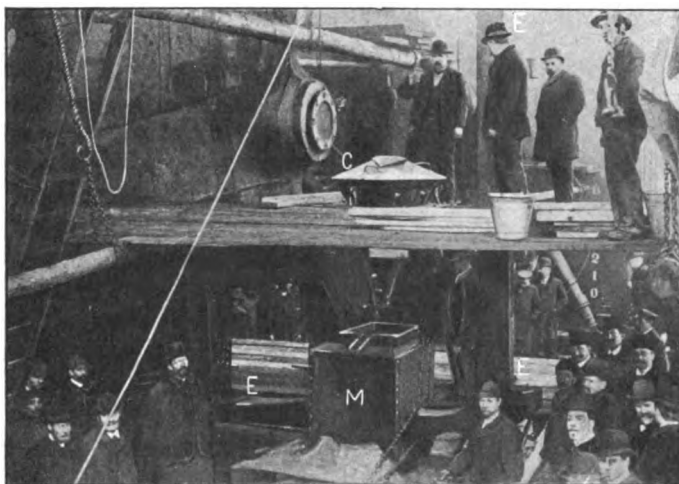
Réparation de l'étambot du Sevilla (avant la coulée). — E, étambot ; C, creuset automatique ; M, moule pour recevoir la coulée.
